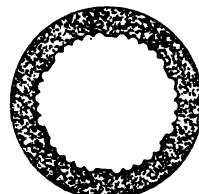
Piepers Zugconstruction für Bürgewehre.
